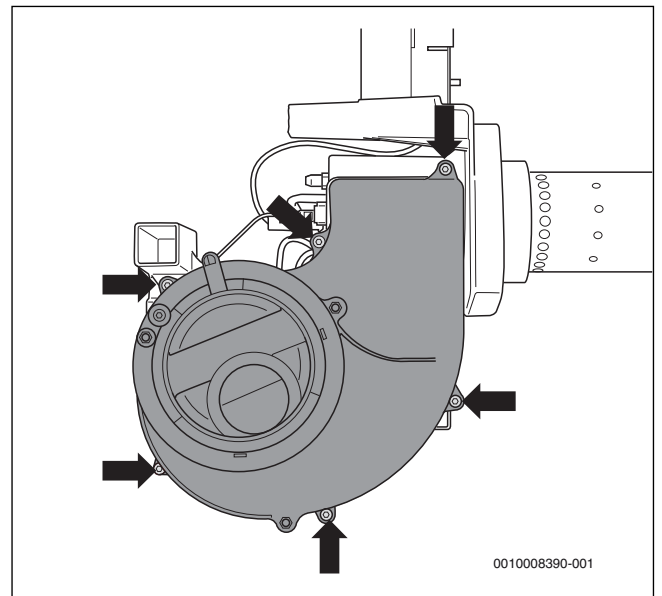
Desmontaje de la cubierta de la turbina del ventilador
